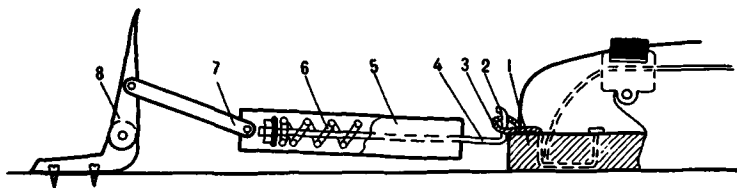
Бестросиковые крепления с пружиной натяжения типа "безмен"
